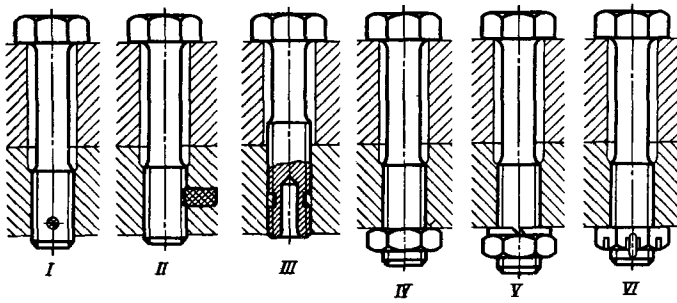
Способы стопорения свертных болтов с нарезного конца:
